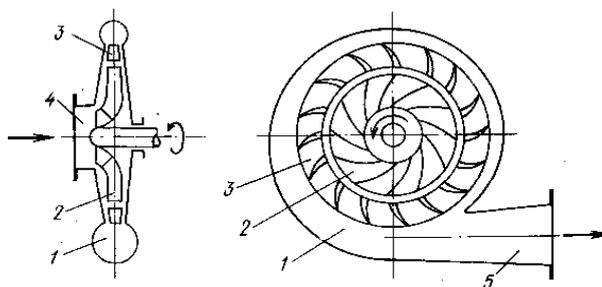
Схема турбогазодувки: 1 – корпус; 2 – рабочее колесо; 3 – направляющий аппарат; 4 – всасывающий патрубок; 5 – нагнетательный патрубок
